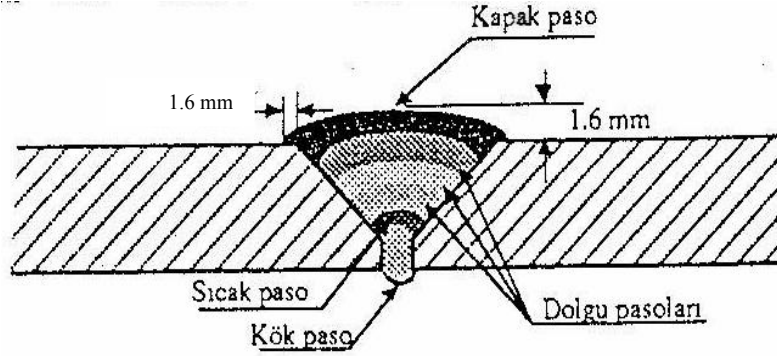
Fitting Boru Alın Kaynağı Montaj Detayı
